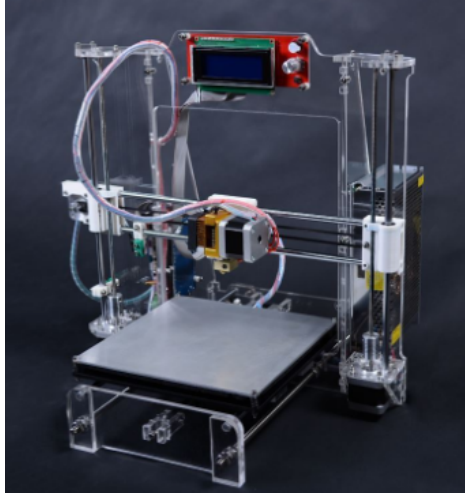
Impresora Geetech I3 fabricada en corte Láser
